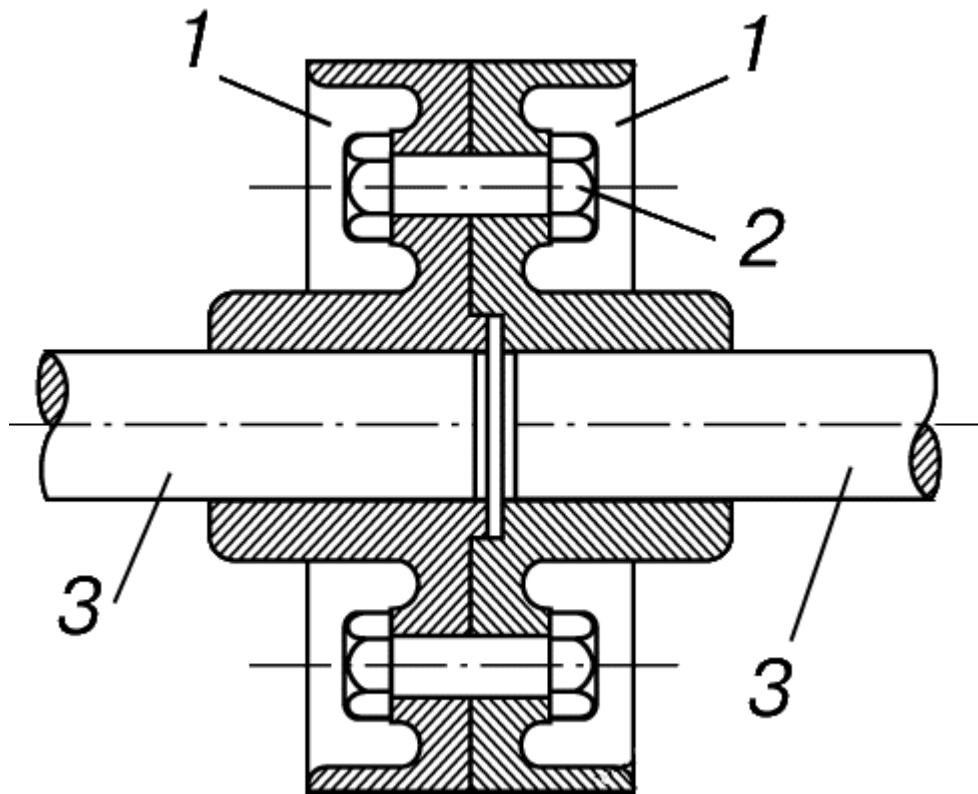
Конструкція фланцевої муфти: 1 – напівмуфти, 2 – болтове з'єднання, 3 – вали
